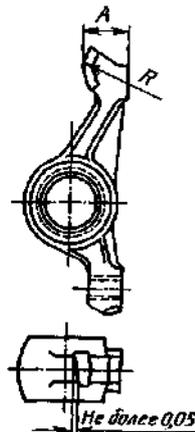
Схема рабочей поверхности бойка коромысла:
